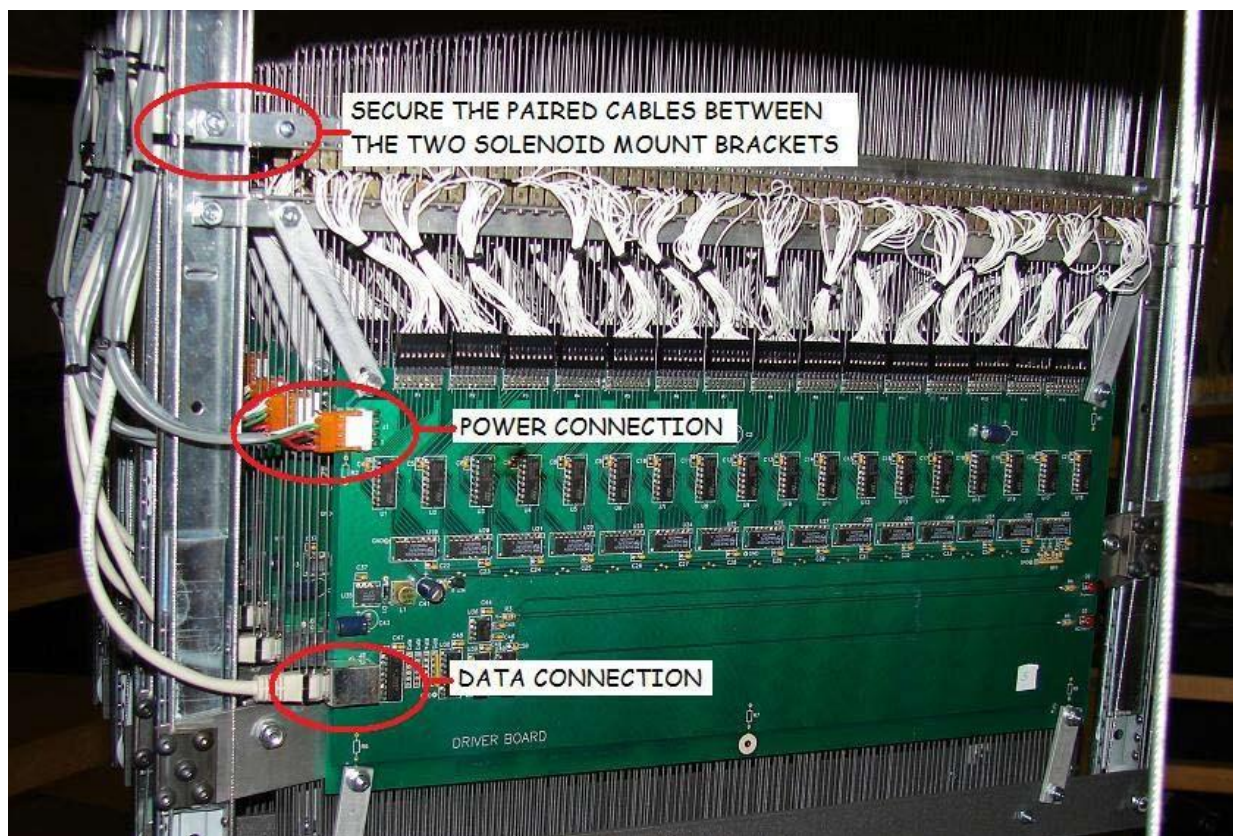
Conexión de cables y fijación a la estructura del módulo
